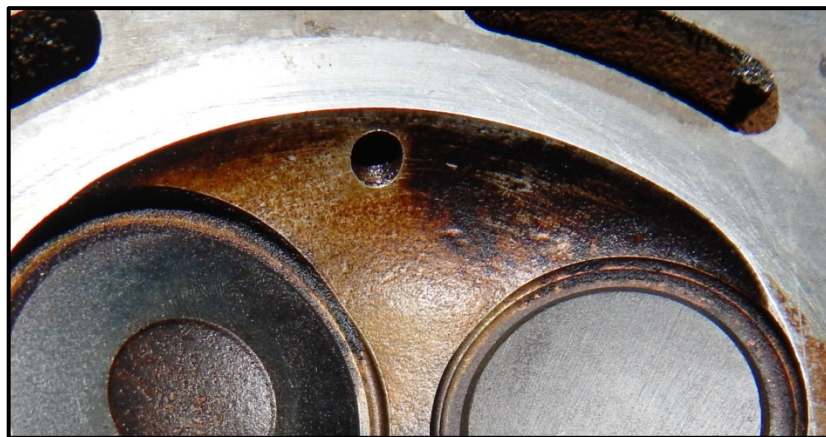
Furo do cabeçote para instalação do sensor de pressão GU22C.
